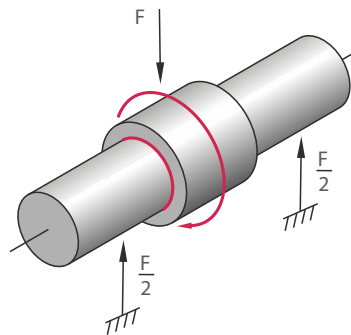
Umfangslast, rotierende Belastung, Welle steht, Buchse dreht sich.
